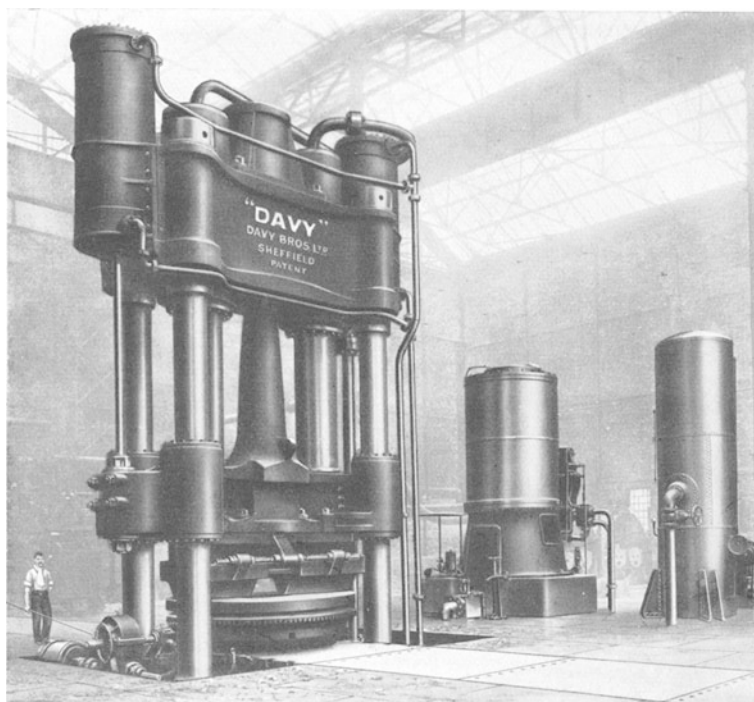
3000 t-Schmiedepresse mit Werkzeugen zum Schmieden von Rädern und Turbinenscheiben. (Davy Brothers Ltd., Sheffield.)
